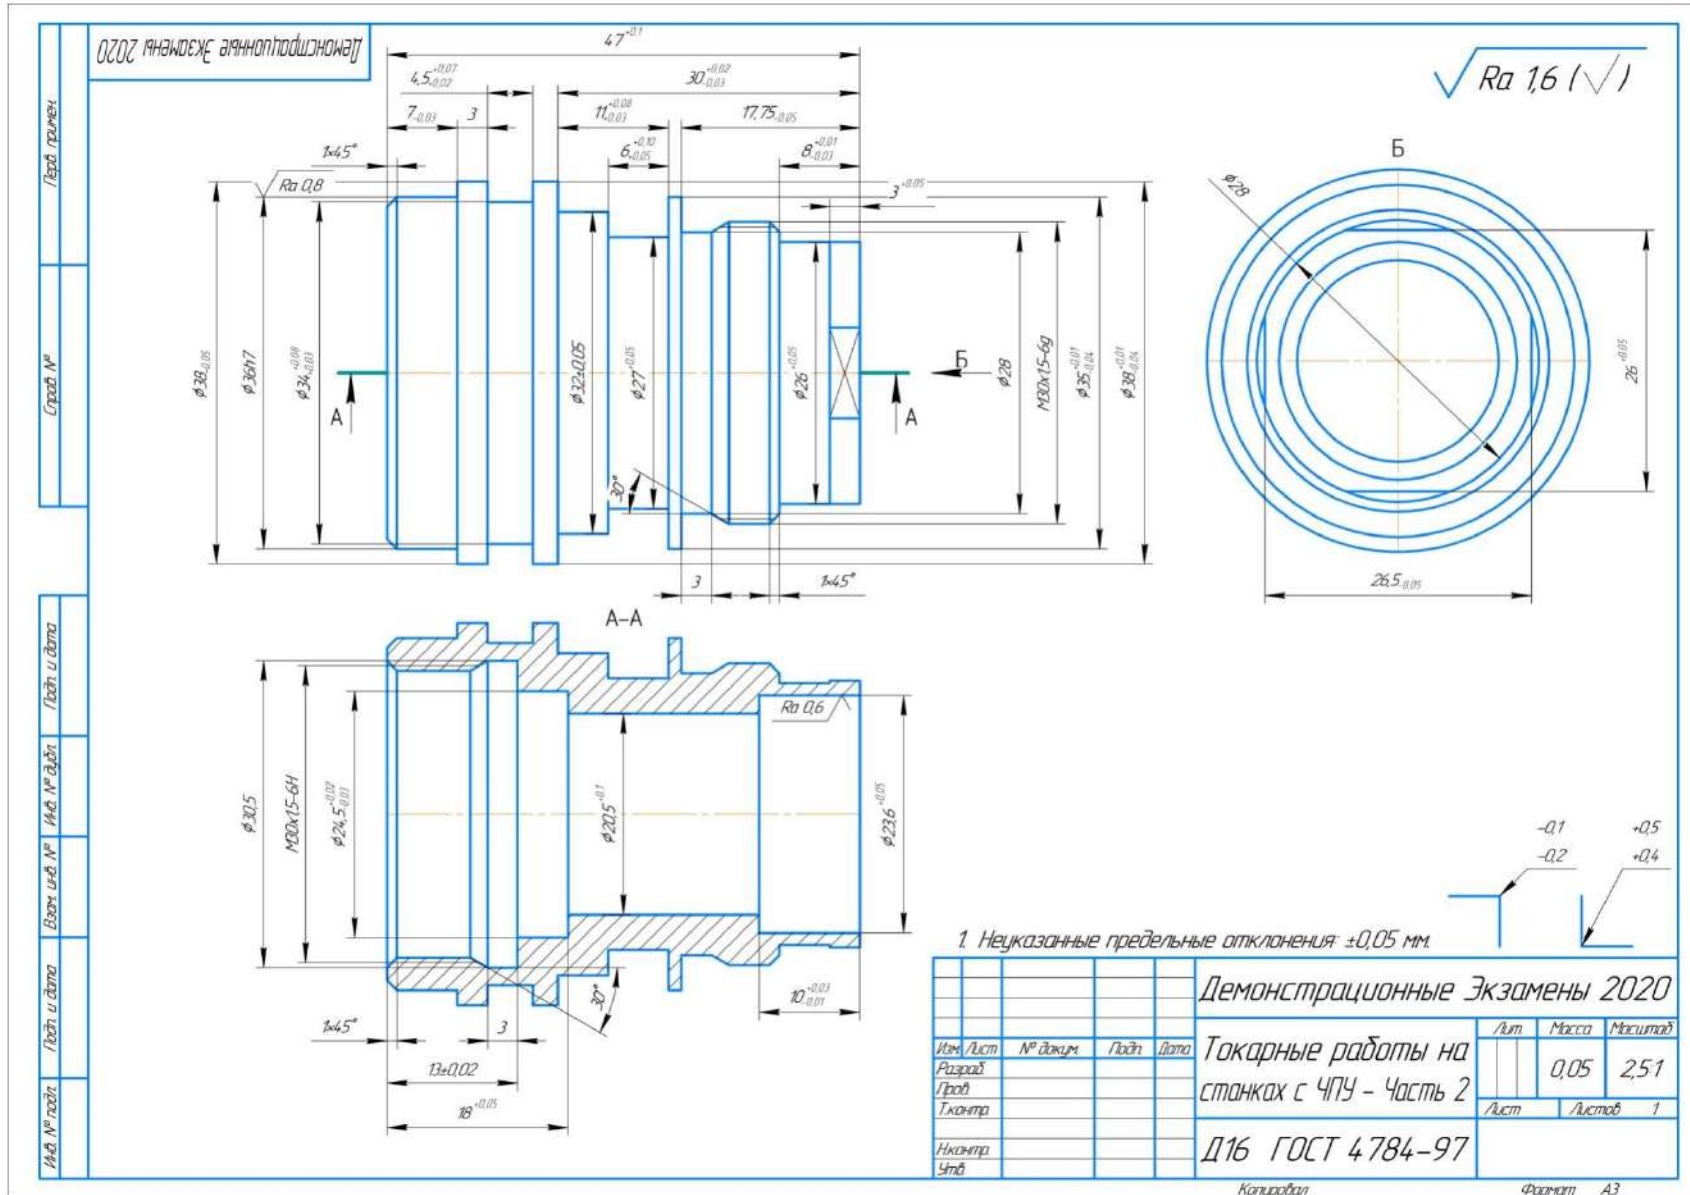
Чертеж детали Токарные работы на станках с ЧПУ
